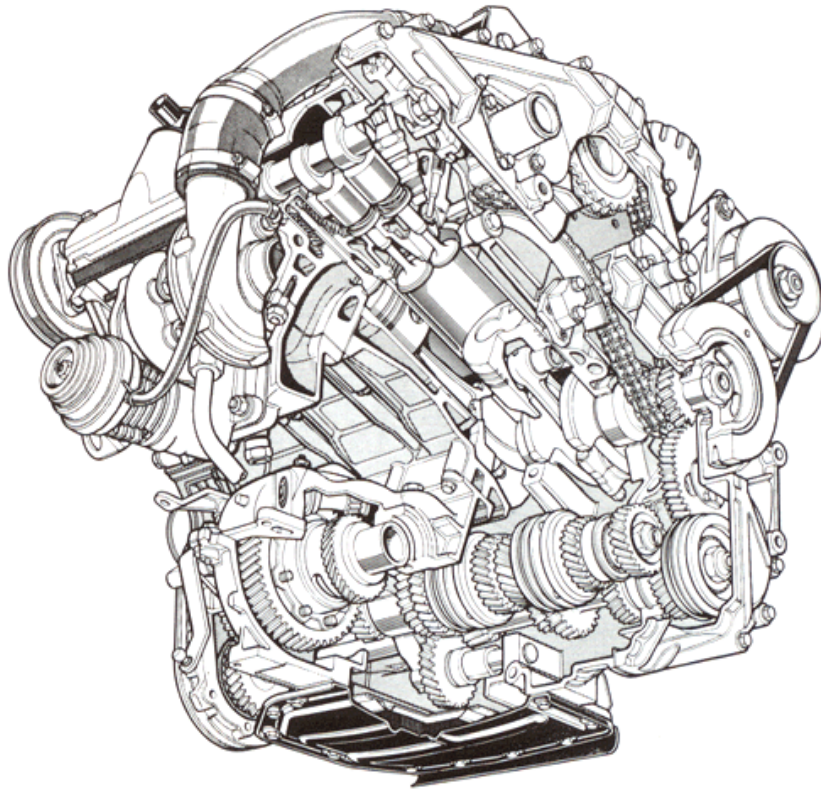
Vista de un motor Diesel VERA, provisto de turbo, fabricado para los motores PEUGEOT de turismo.
